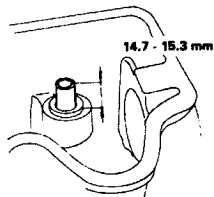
Выступ направляющей втулки над поверхностью головки блока цилиндров (См. Раздел 17)
